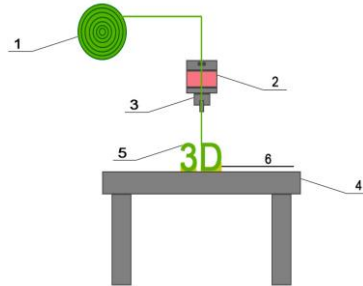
Зображення схеми FDM [1]: 1-катушка з матеріалом; 2- друкуюча головка; 3-сопло; 4- робочий стіл 3 D -принтера; 5- надрукований об'єкт; 6- підтримки
